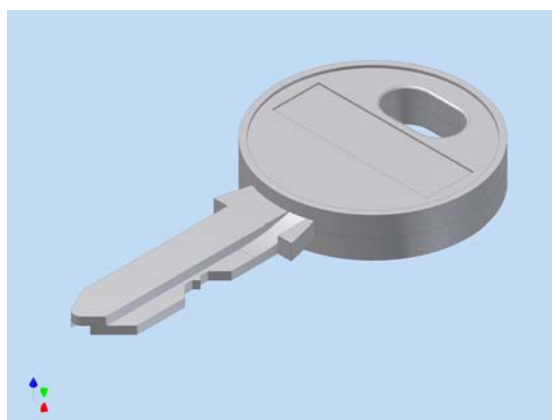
Модель сборки, импортированная из Pro/ENGINEER.
